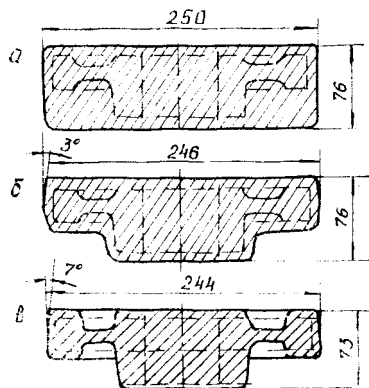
Виды заготовок зубчатого цилиндрического колеса
